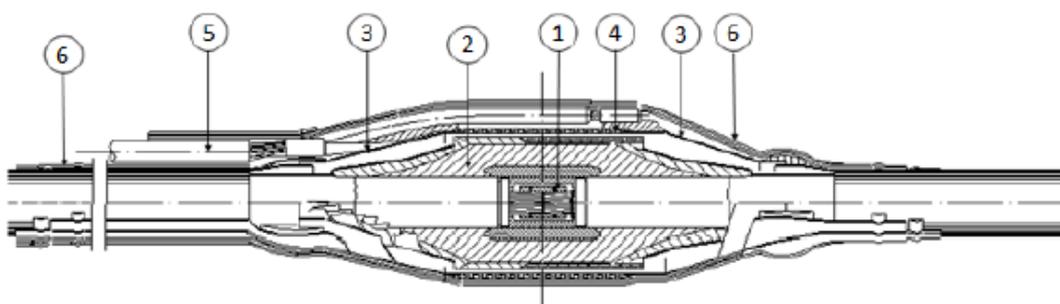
Empalme seccionado o con interrupción de pantalla
